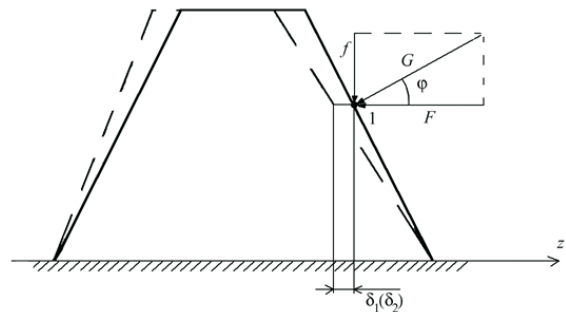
Третий уровень декомпозиции резьбового соединения (виток резьбы болта и гайки).
